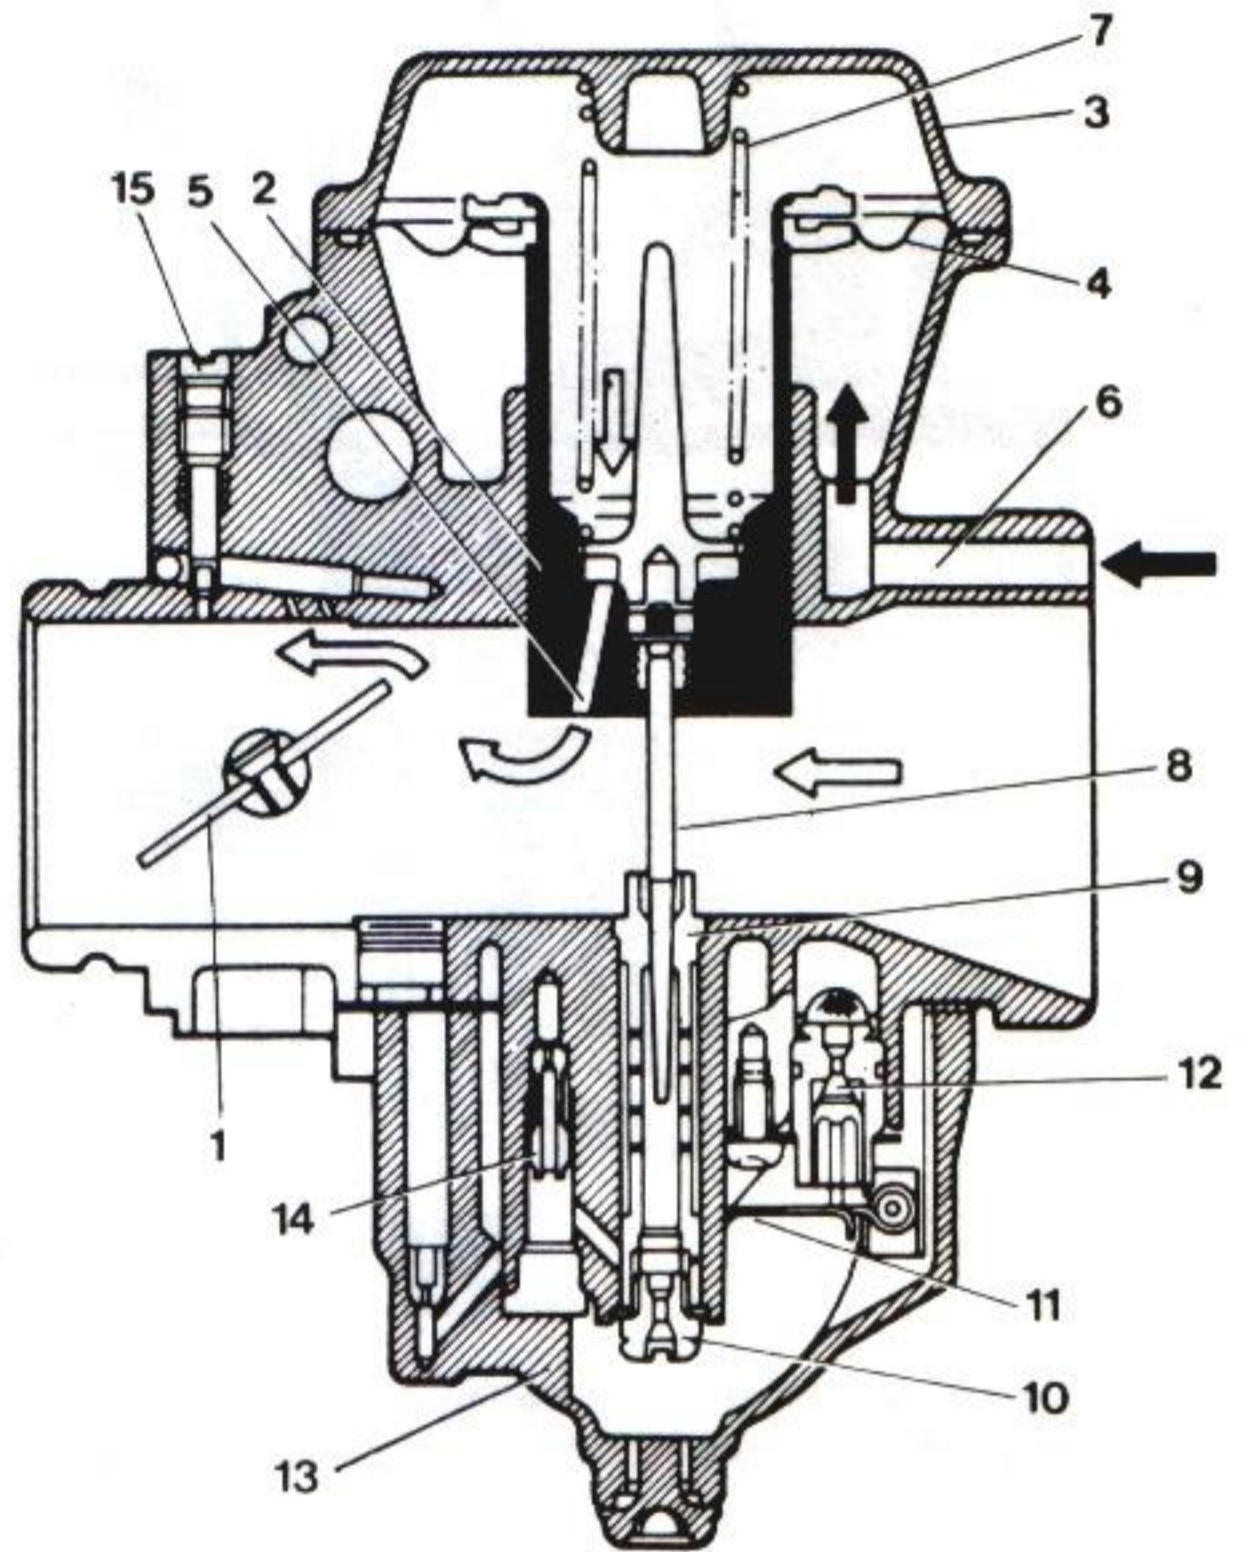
Esquema de un carburador de cápsula de depresión de la marca japonesa MIKUNI. La válvula corredera funciona según el estado de la depresión dentro de la cámara de la parte alta, mientras la aceleración la realiza el conductor actuando sobre la válvula de mariposa (1); 2, válvula corredera de depresión; 3, cápsula; 4, membrana; 5, orificio; 6, conducto; 7, muelle; 8, aguja cónica; 9, tubo de emulsión; 10, surtidor principal; 11, flotador; 12, válvula de aguja; 13, cuba; 14, surtidor de marcha lenta; 15, tornillo regulador de riqueza de marcha lenta.
